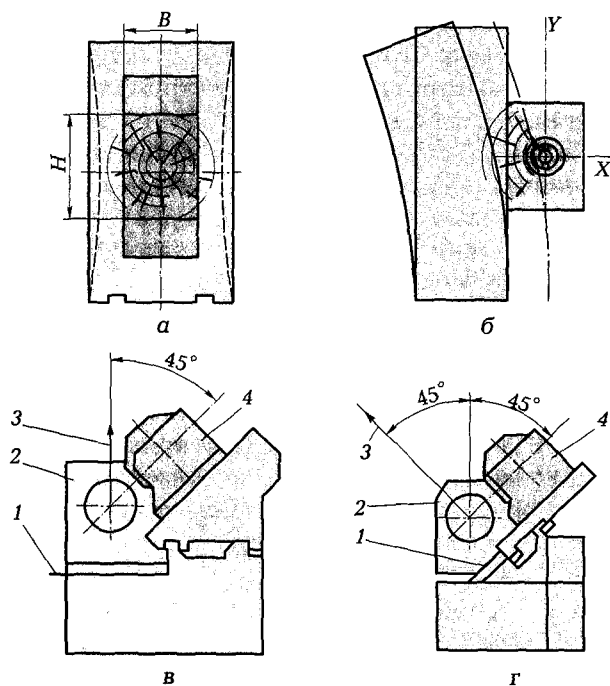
Виды компоновок шпиндельных бабок на многоцелевых и токарных станках с ЧПУ:
